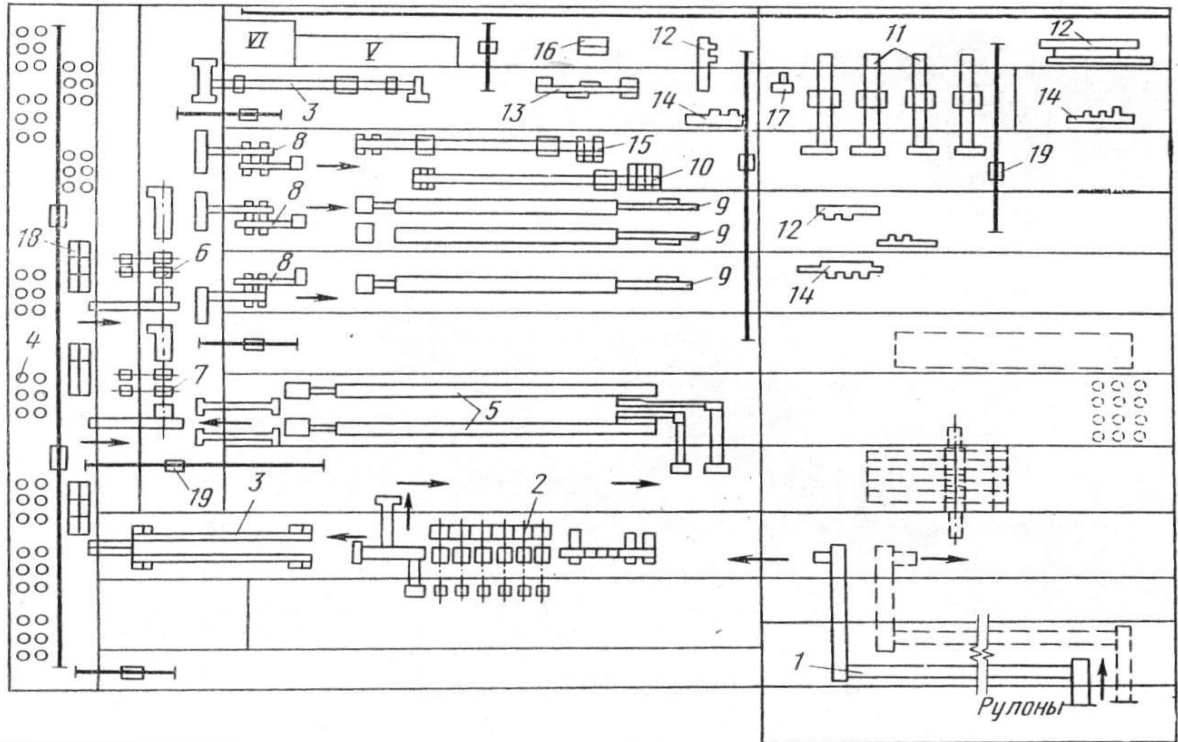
План цеха з шестиклітьовим станом 1400 нескінченної прокатки конструкції УЗВМ: 1 – безперервний правильний агрегат; 2 – шестиклітьовий чотиривалковий стан холодного прокатування 1400; 3 – агрегати електролітичної очистки; 4 – ковпаків печі; 5 – безперервні агрегати відпалу; 6,7 – двоклітьовий дресирувальний стан 1400; 8 – агрегати підготовки рулонів; 9,10 – агрегати електролітичного луження і хромування; 11 – агрегати поперечного розрізання; 12 – агрегати упаковки пачок жерсті; 13 – агрегати упаковки рулонів; 14 – сортувальні агрегати; 15 – агрегати вакуумного алюмініювання; 16 – ножиці; 17 – ваги; 18 – стенди охолодження рулонів; 19 – поперечні візки
